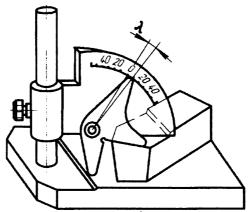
Схема измерения угла λ токарного проходного резца
